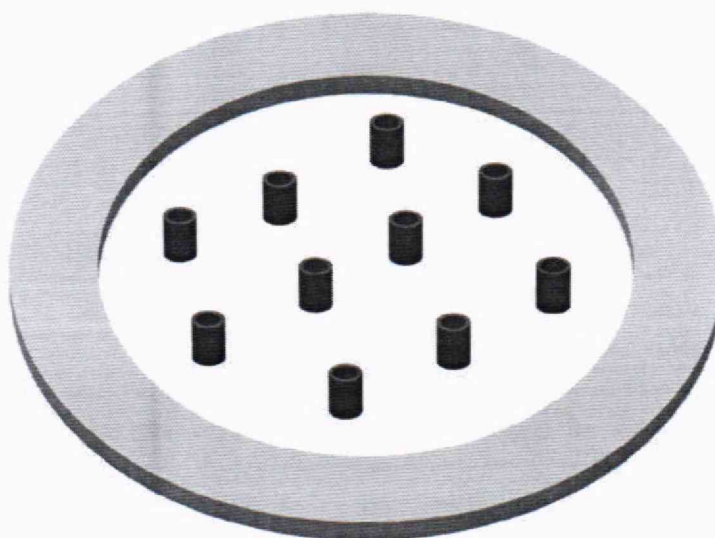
Схема установки алюминиевых втулок внутри вспомогательного кольца
